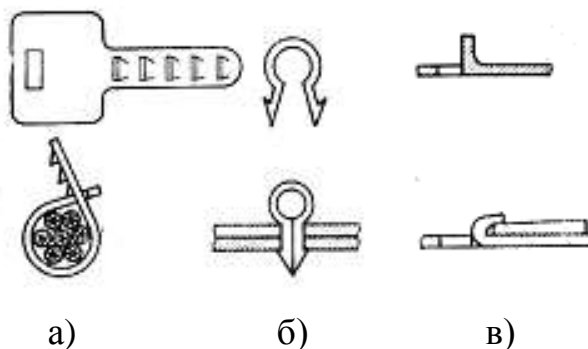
Способи безгвинтового з'єднання деталей:
